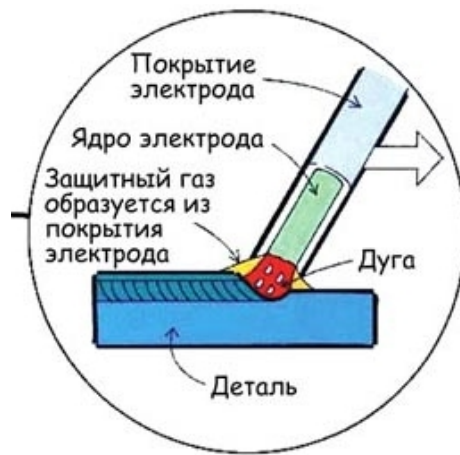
Схема дуговой сварки штучными электродами
